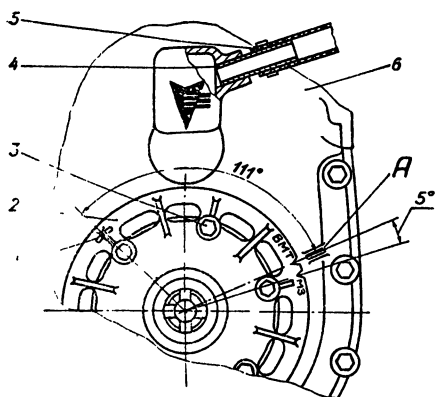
Установочные метки на шкиве центробежного маслоочистителя и крышке распределительных шестерен:
